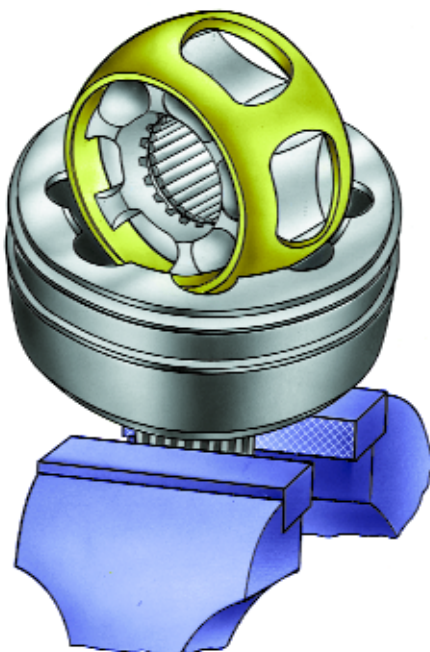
Извлечение сепаратора с обоймой из наружного шарнира
